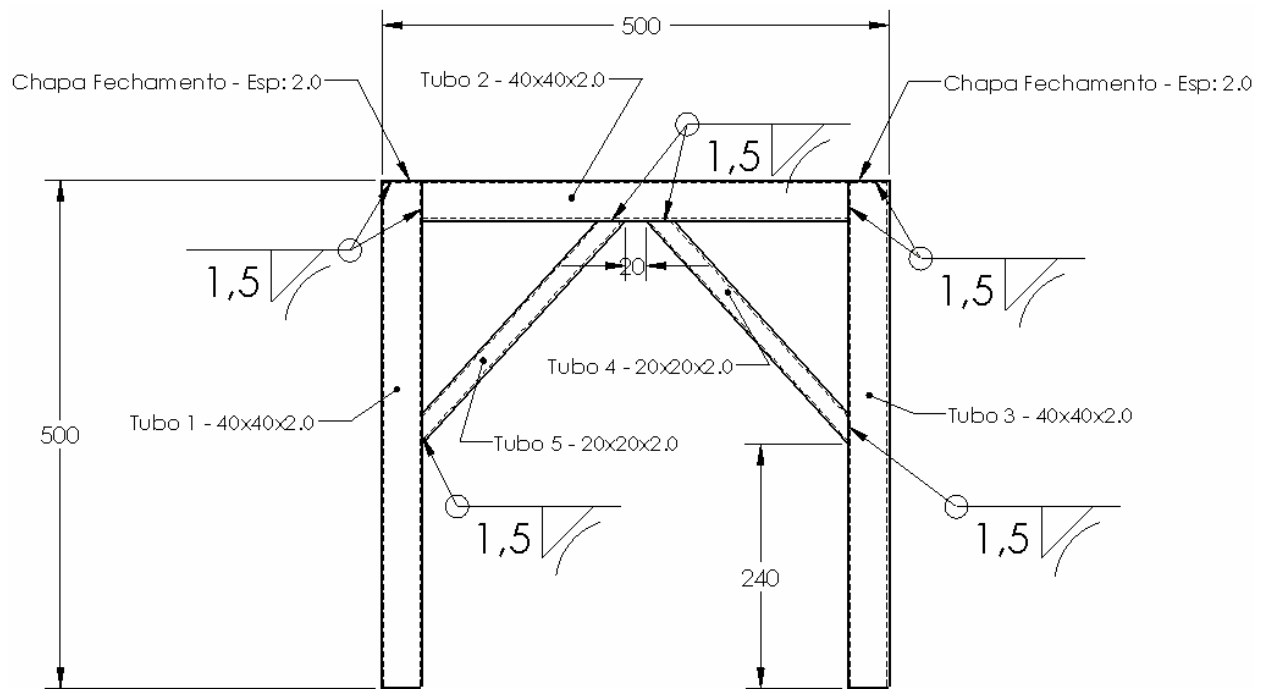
Estrutura tubular soldada utilizada nos modelos dos exemplos da seção 2.4.
